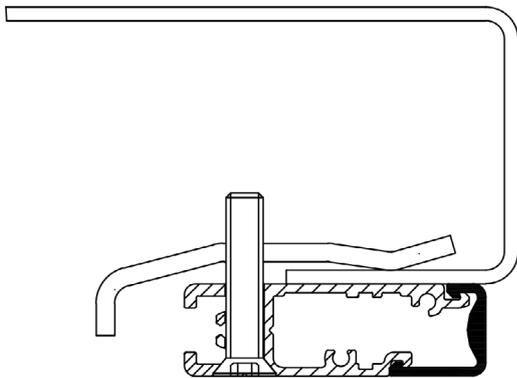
Perfil de 10 mm montado con una placa de fijación
